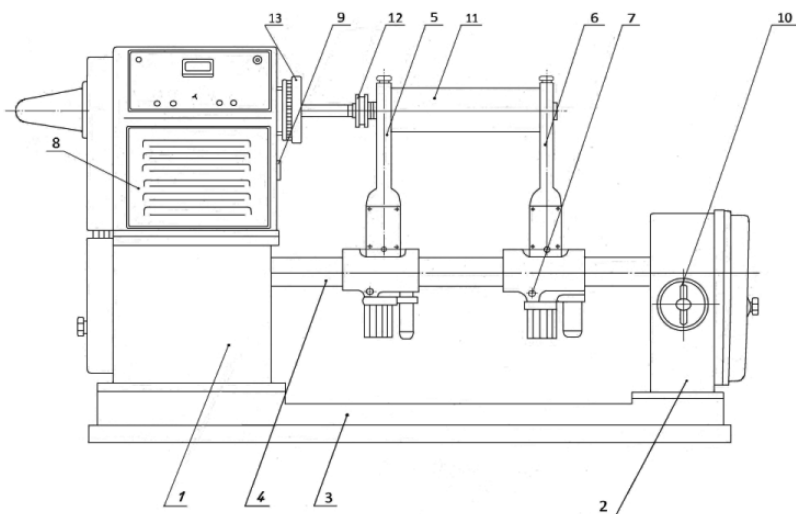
Станок для динамической балансировки деталей модели КИ-4274
